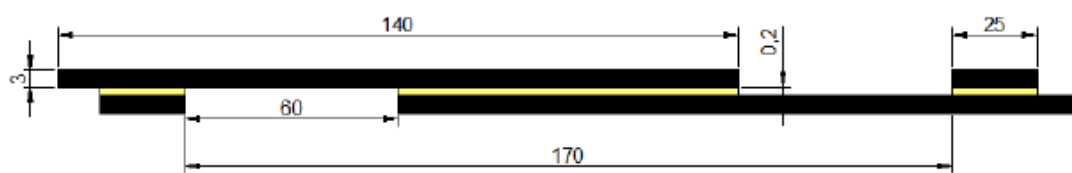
Geometria e dimensões das juntas de L_0 de 50 mm [99]
